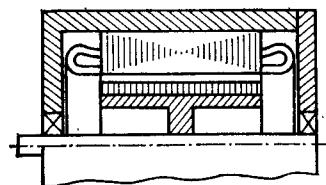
Конструктивная схема субсинхронного реактивного двигателя
